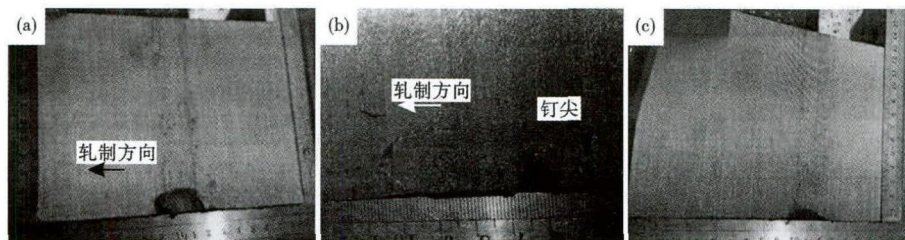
3#钉子在轧件中的剖面状态:离底部62.7 mm(17 mm×32 mm)(a);59.7 mm(20 mm×55 mm)(b);57.7 mm(Φ30 mm 半圆坑)(c)
